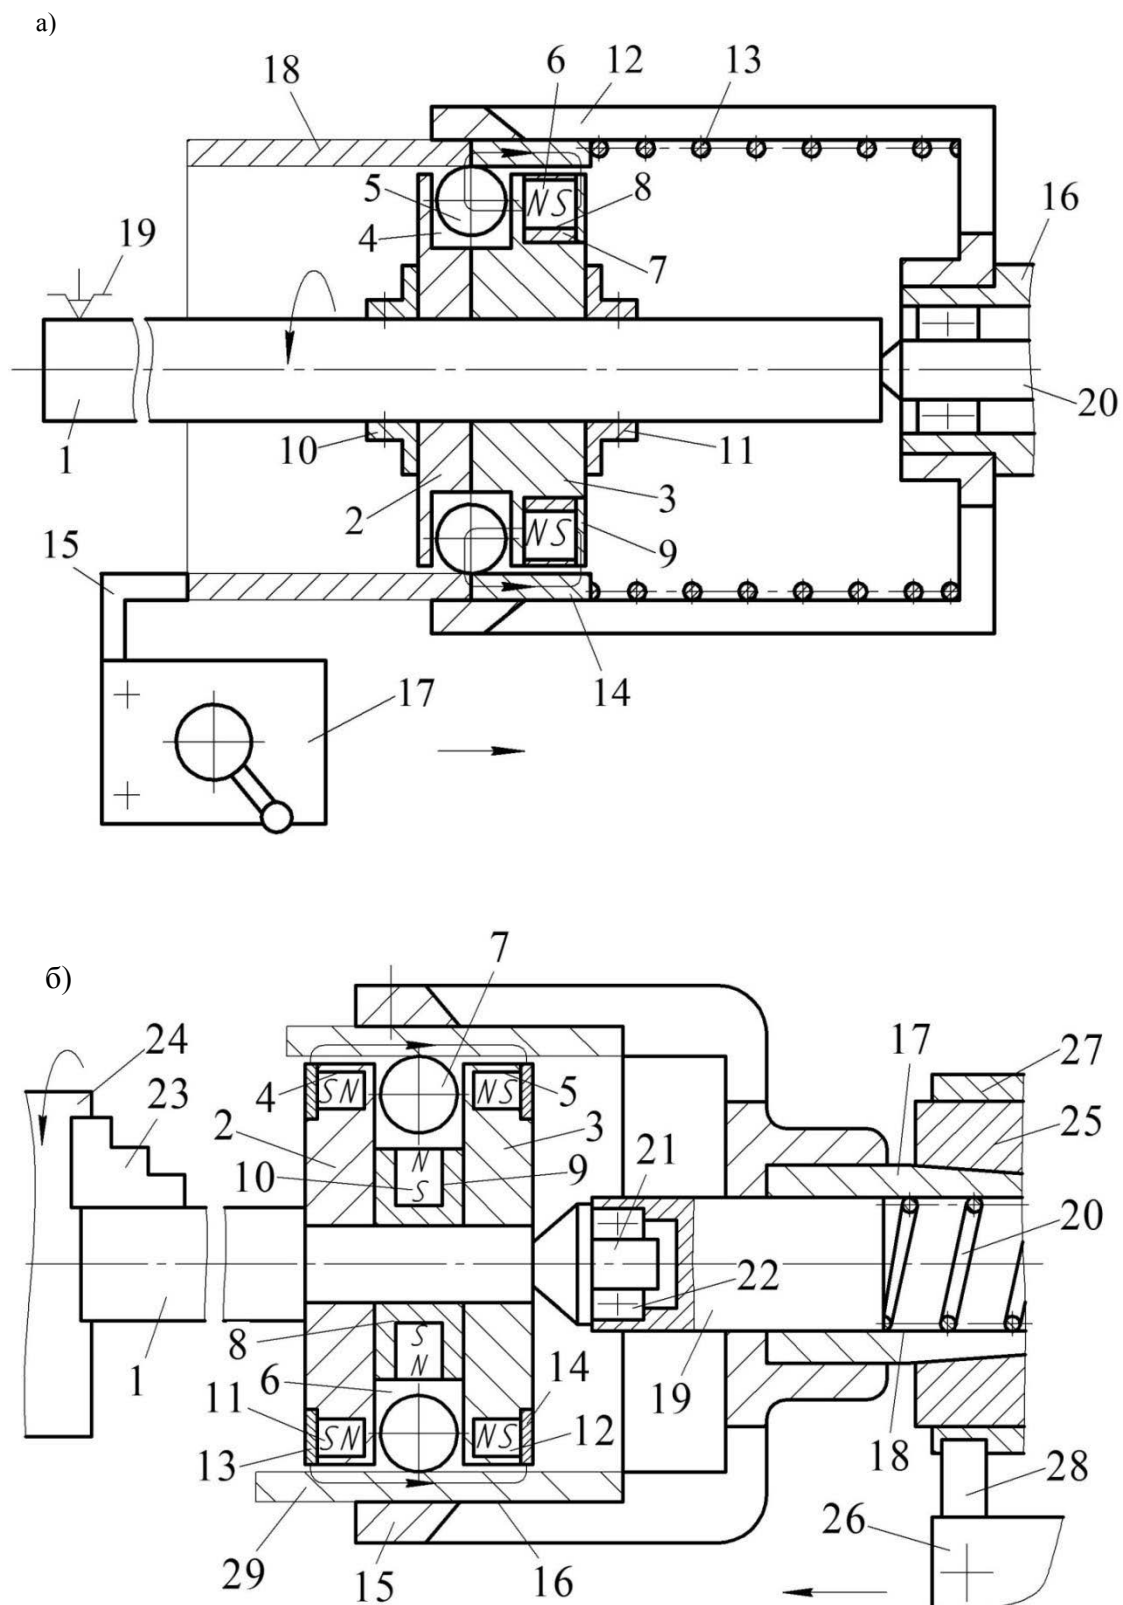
Конструкции инструментов для СМДН внутренней поверхности цилиндров на станках токарной группы: а – для обработки крупногабаритных цилиндров; б – для обработки малогабаритных цилиндров
